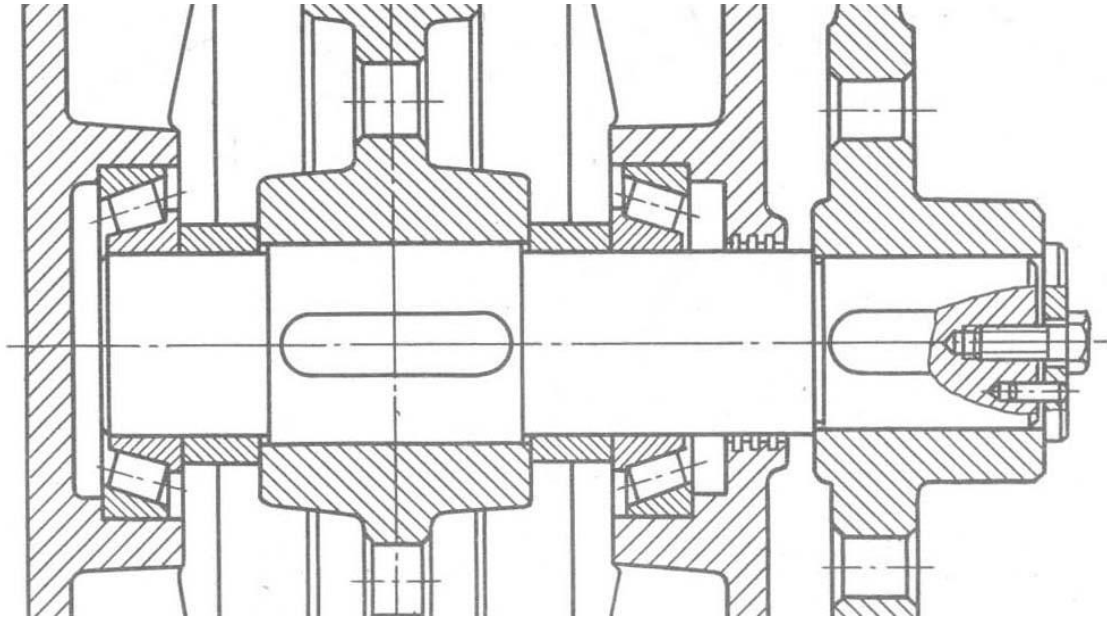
Складальний кресленник вузла вихідного валу редуктора
